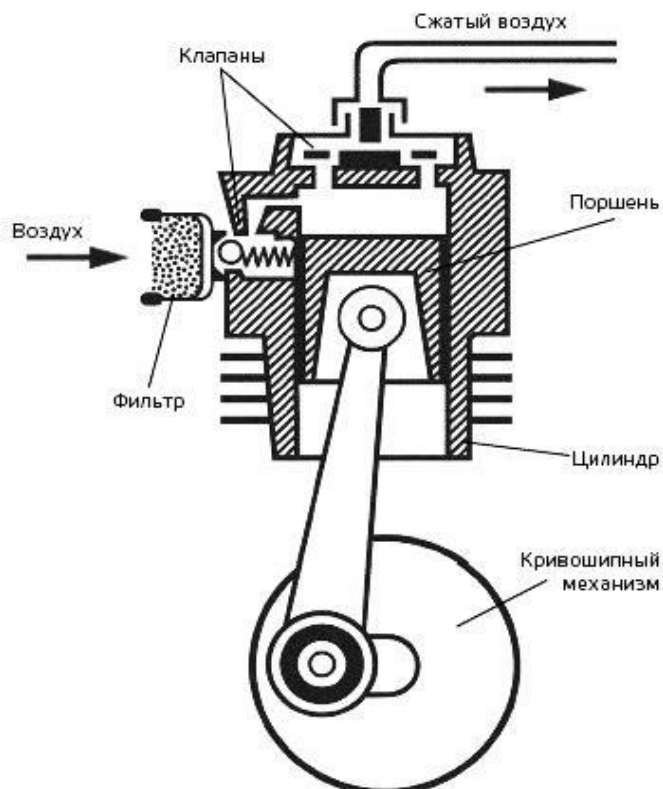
Одноступенчатый поршневой компрессор бескрейцкопфного типа
